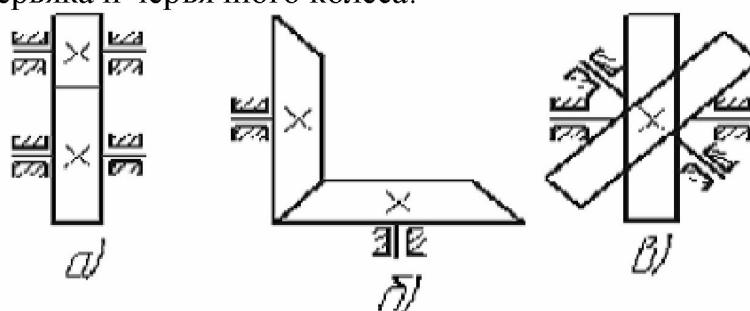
Кинематические схемы зубчатых передач: а – цилиндрическая; б – коническая; в – гиперболоидная
